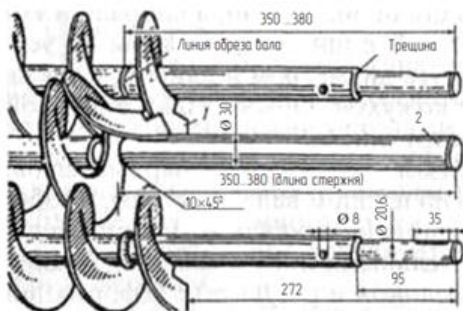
Ремонт вала шнека приваркой стержня: 1 – конец спирали; 2 – стержень
